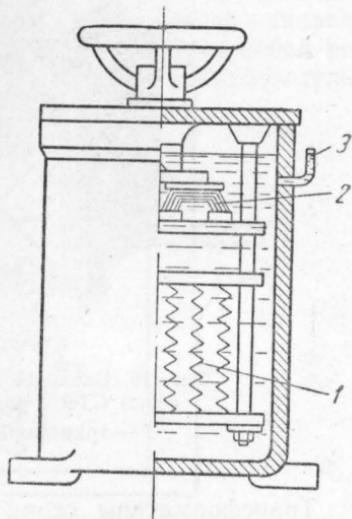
Внешний вид сварочного аппарата серии СТН в однокорпусном исполнении.
